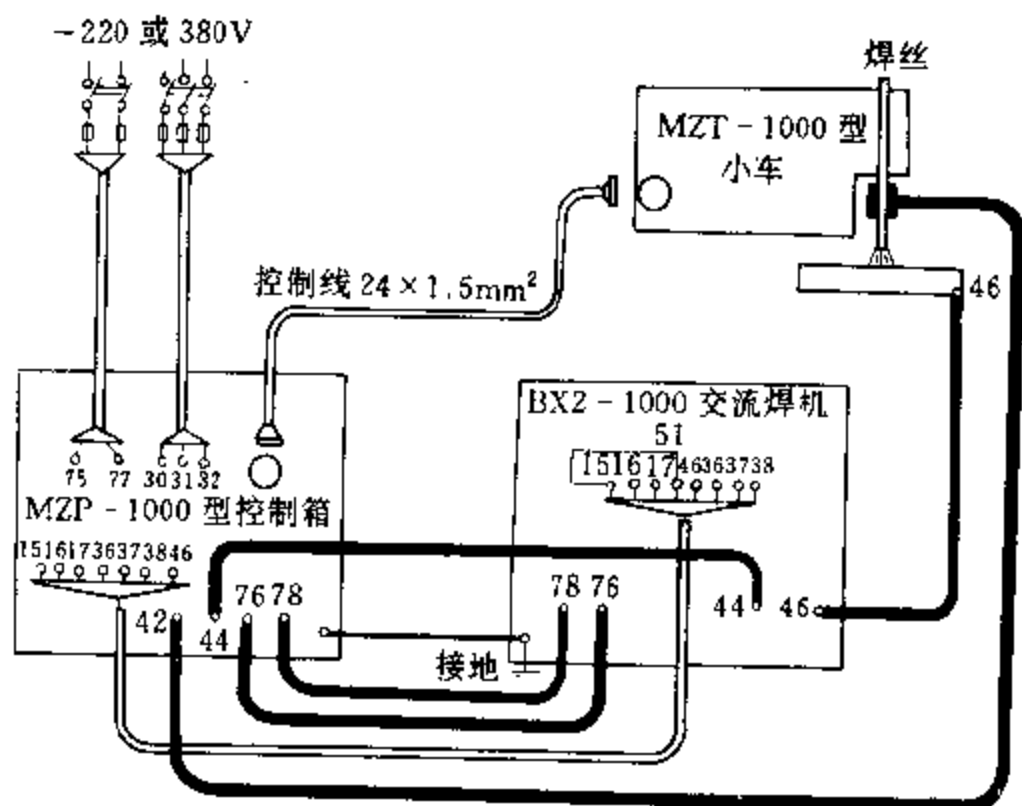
用交流电源时 MZT-1000 型焊机的外部接线图
